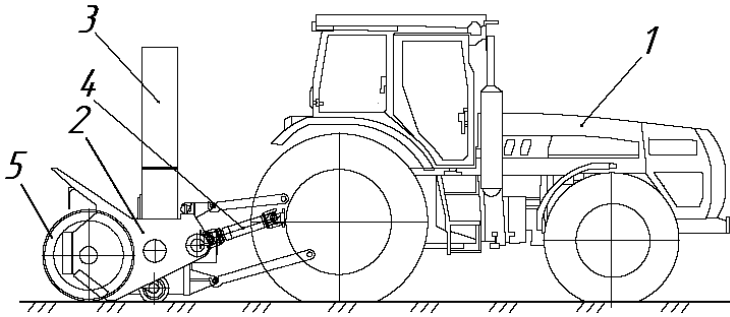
Конструктивная схема снегоочистителя «Амкодор-9513»: 1 – базовый трактор; 2 – корпус рабочего органа; 3 – погрузочный желоб; 4 – карданный вал; 5 – фреза
